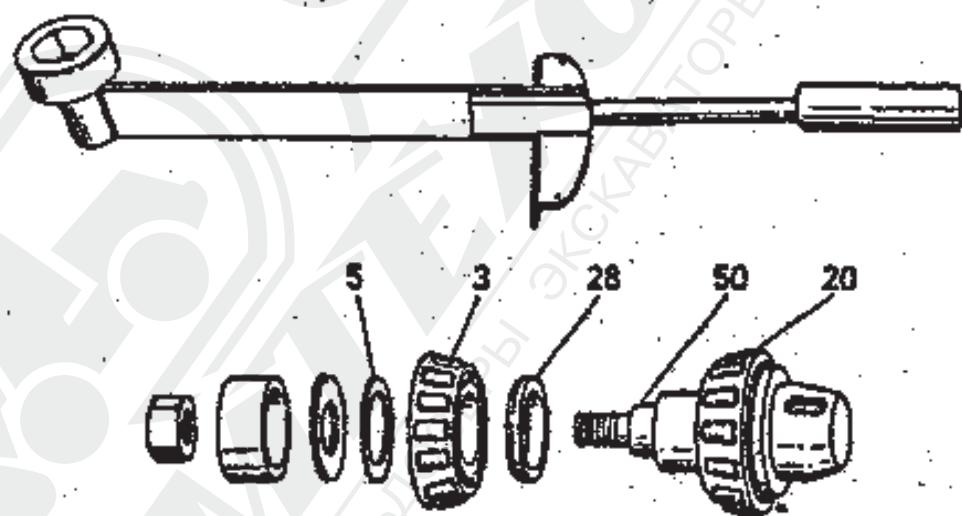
Элементы узла приводного колеса вмонтированные в прибор 3, 20 - конический роликоподшипник,
